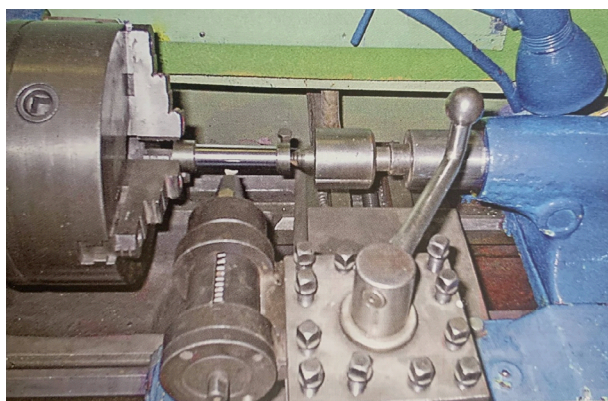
Внешний вид устройства для нанесения антифрикционных покрытий
